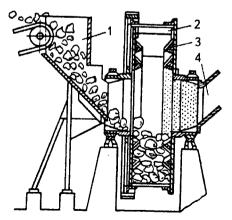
Мельница сухого самоизмельчения «Аэрофол»: 1 – эагрузочная течка; 2 – поперечные била; 3 – зубчатые выступы; 4 – разгрузочный патрубок
